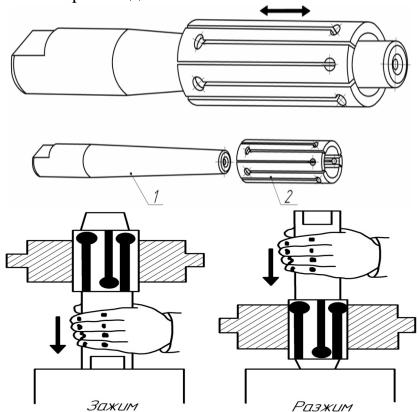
Центровая разжимная ручная оправка: 1 — оправка, 2 — цанговая втулка
